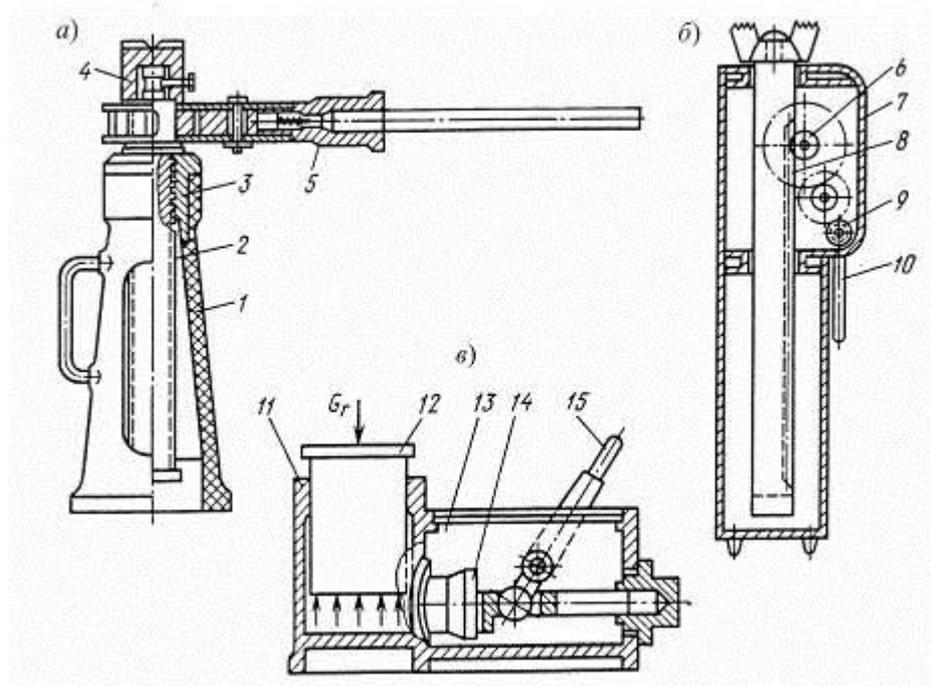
Домкраты: а — винтовой; б — реечный; в — гидравлический; 1,7 — корпуса; 2 — винт; 3 — гайка; 4 — головка винта; 5, 10 — рукоятки; 6 — шестерня; 8 — зубчатая рейка; 9 — зубчатое колесо; 11 — цилиндр; 12 — поршень; 13 — резервуар для гидравлической жидкости; 14 — плунжерный насос; 15 — рычаг
